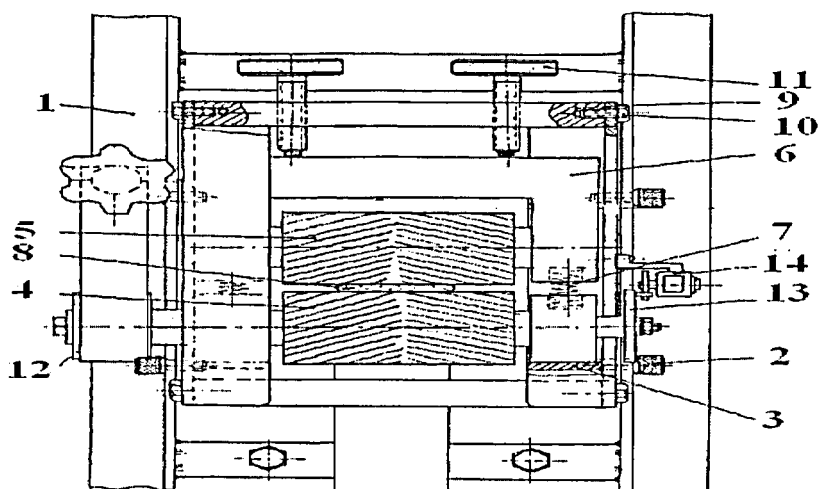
Тренажёр «Мини-канат» для сопряжённого развития скоростно-силовых способностей борцов (1 – две металлических направляющих, 2 – скрепляющие болты, 3 – опорные пластины, 4 – обрезиненный валик, 5 – обрезиненный валик, 6 – кронштейн, 7 – спиральные пружины, 8 – тканевой круг (борцовский пояс), 9 – прижимная пластина, 10 – болт, 11 – винты, 12 – тормозной барабан, 13 – диск, 14 – динамометр).
